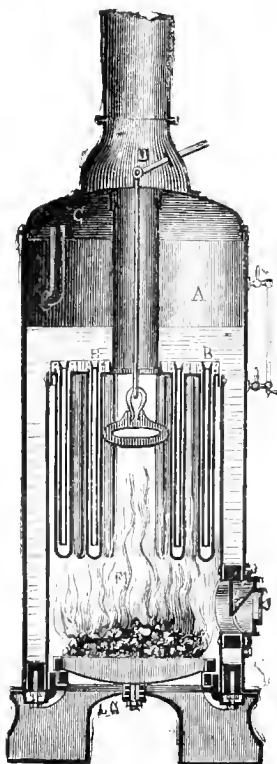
Coupe verticale de la chaudière du moteur fixe de MM. Leccointe et Villette.
